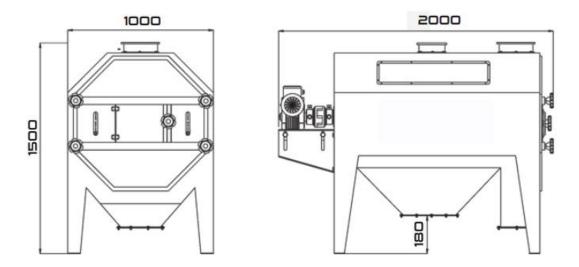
Dimensiones de la máquina de tamiz de tambor.
